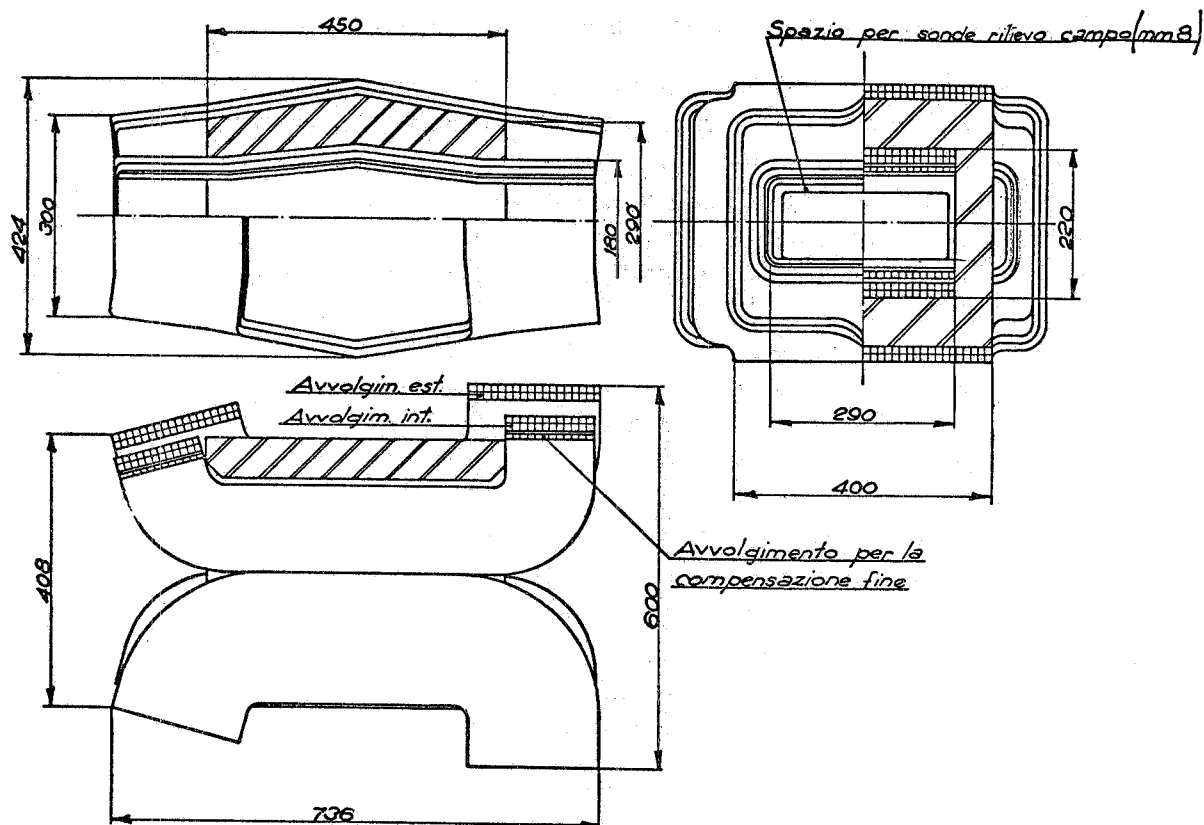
Disegno d'assieme di un compensatore del magnete trasversale.
